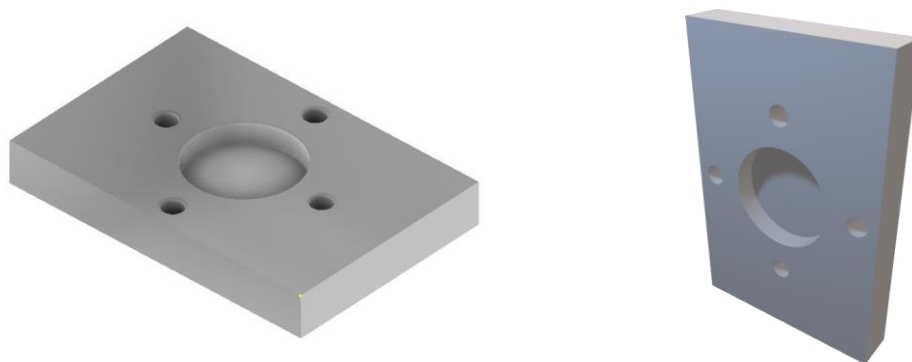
Τρισδιάστατη απεικόνιση αποστολής 30
